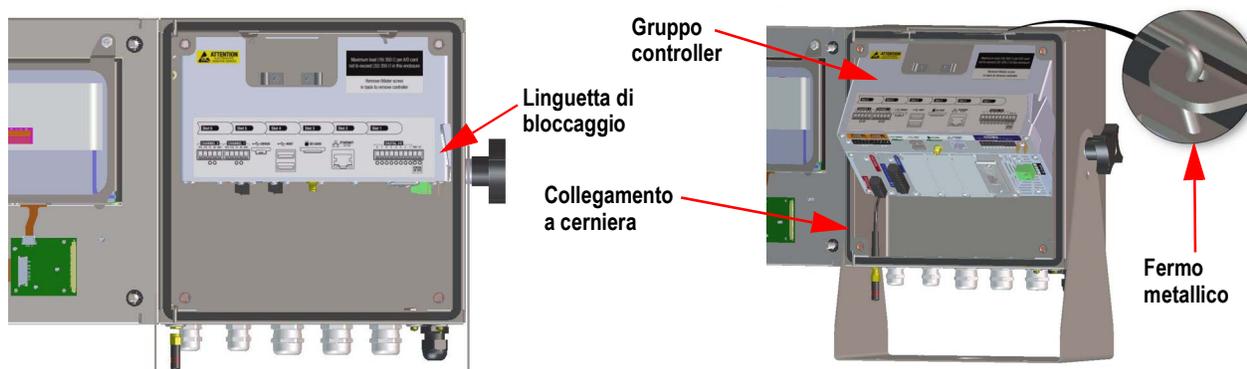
Rimozione del gruppo CPU – Involucro universale
